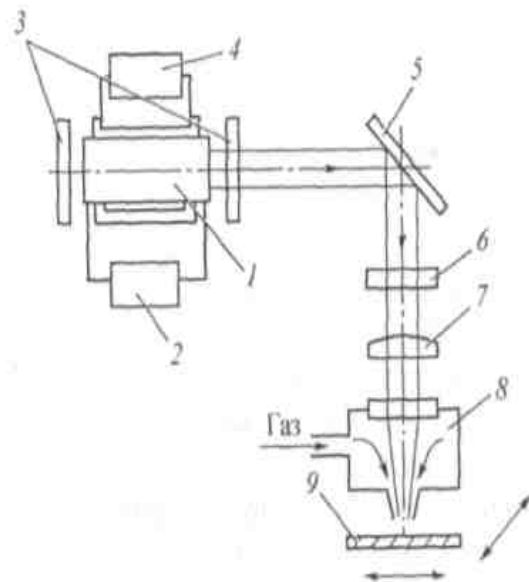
Схема процесса лазерной обработки: 1 — активная среда; 2 — система накачки активной среды; 3 — резонатор; 4 — система охлаждения; 5 — зеркало; 6 — заслонка; 7 — фокусирующая система; 8 — система подачи газа; 9 — обрабатываемая деталь
